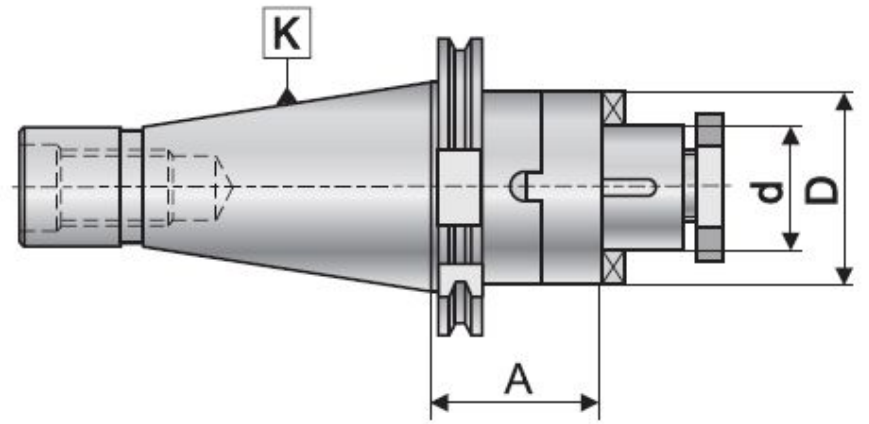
Общий вид системы вспомогательных инструментов для сверлильных и фрезерных станков с ЧПУ
